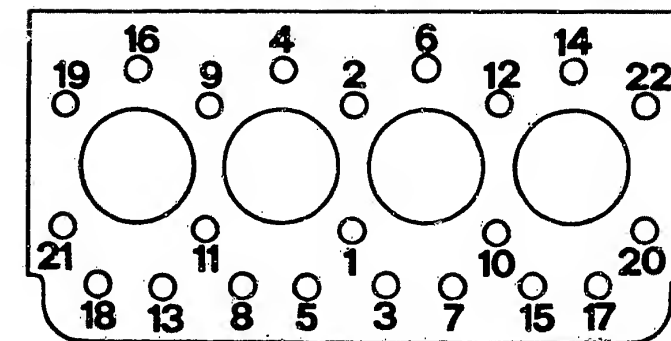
Motor 2500 turbo ds: Anzugsreihenfolge der Zylinderkopfschrauben.
